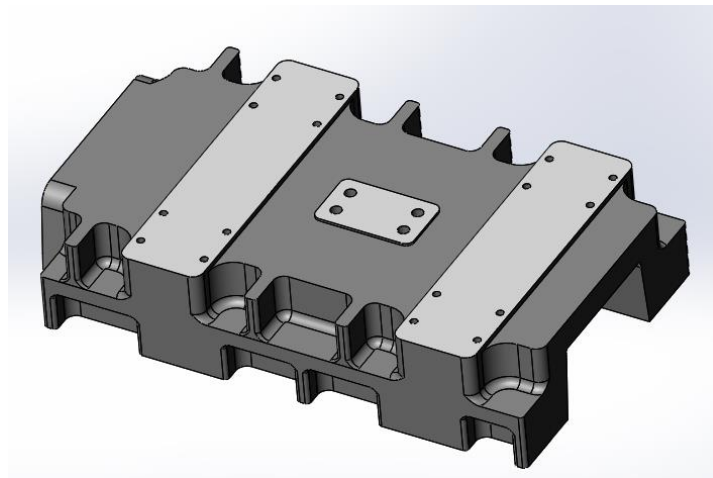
Контактні поверхні для корпусу гайки ШВП та кареток поперечного руху столу
